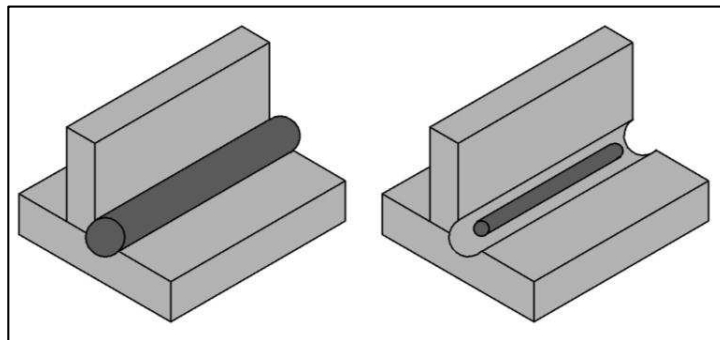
Expansión y Contracción de la Soldadura.
